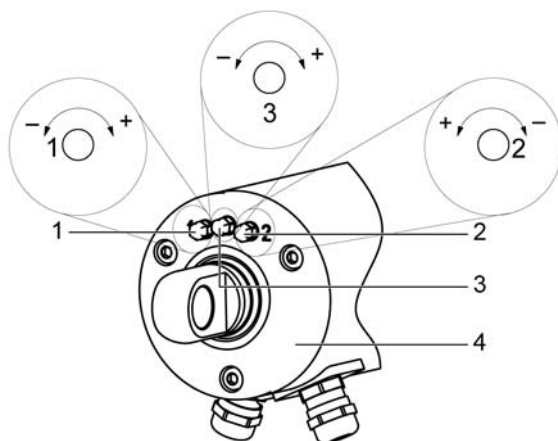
Tapa con tornillo regulador 3 (posición intermedia)
